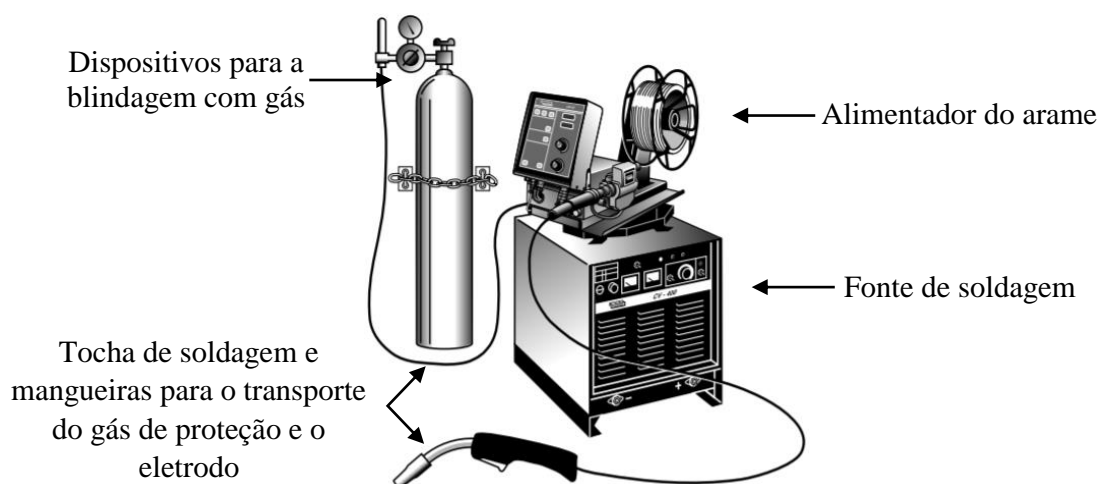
Equipamentos básicos de soldagem GMAW (modificado Nadzam, 2011).
